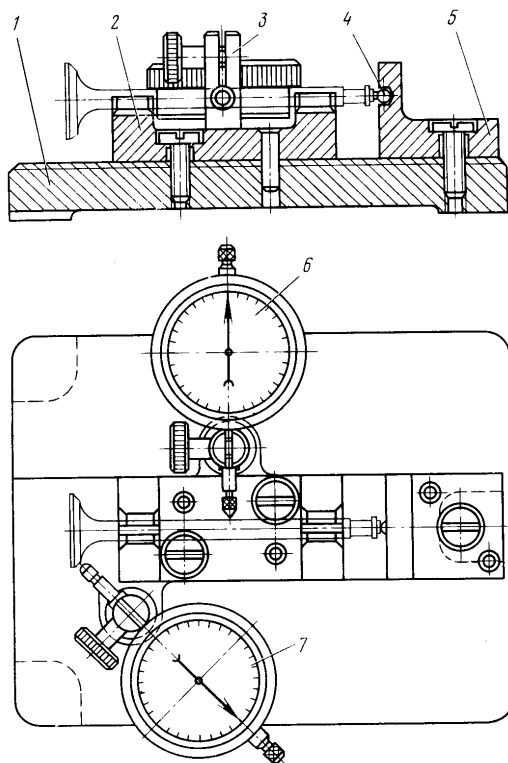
Проверка клапана на concentричность рабочей фаски головки и стержня:
